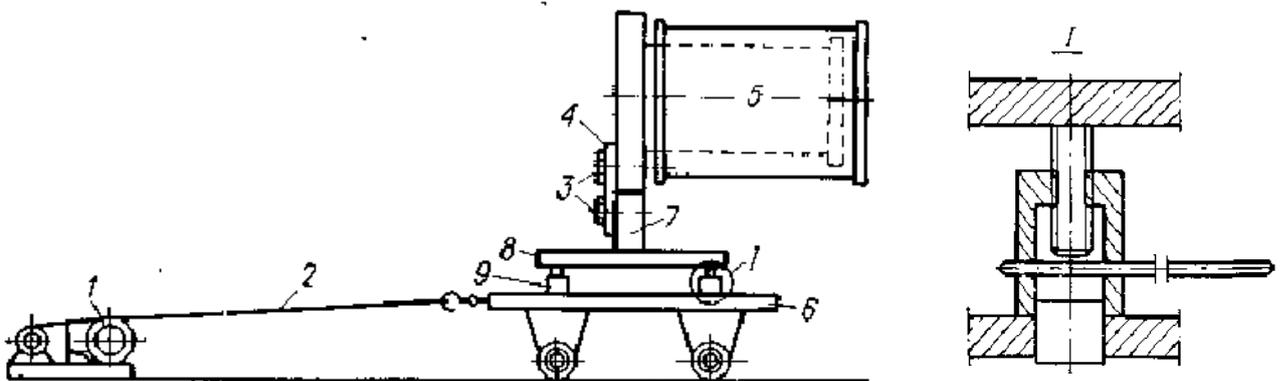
Приспособления для извлечения трубчатki из горизонтального теплообменника: 1 – лебедка; 2 – трос; 3 – болты; 4 – соединительная планка; 5 – теплообменник; 6 – тележка; 7 – опорный сухарь; 8 – плита; 9 – домкрат для подъема опорной плиты.
